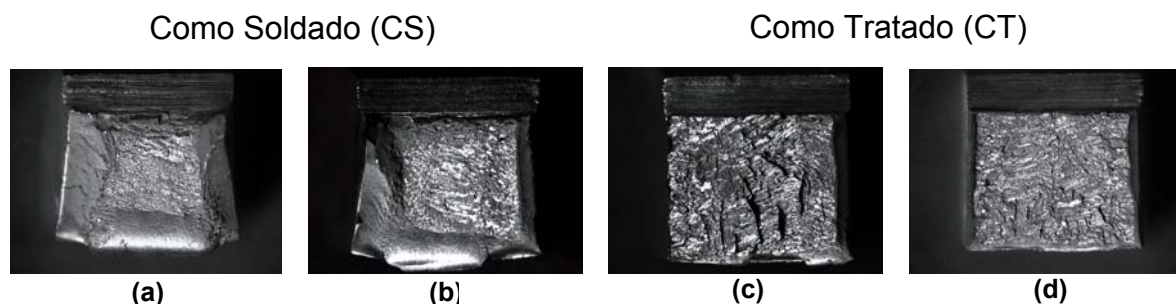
Aparência da Fratura dos Corpos de Prova Charpy, conforme ASTM E-23 (a) Solda Raiz CS, 106J, 74% Dúctil; (b) Solda 2mm da Face CS, 72J, 53% Dúctil; (c) Solda Raiz CT, 12J, 17% Dúctil; (d) Solda 2mm da Face CT, 17J, 18% Dúctil.
